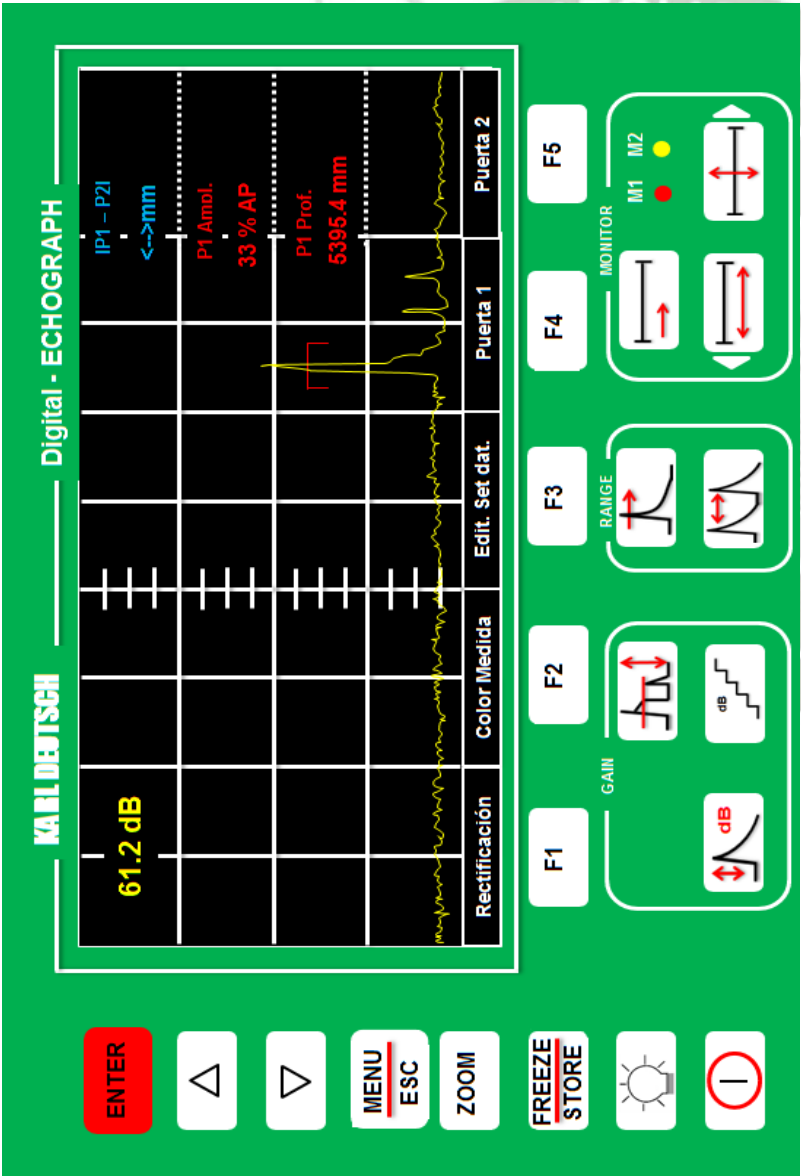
Pantalla de Inspección 2 lado izquierdo
